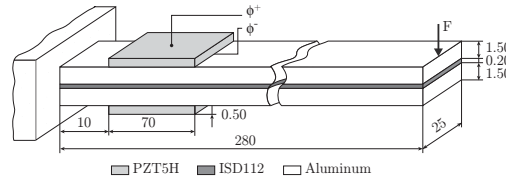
Caractéristiques de la poutre sandwich (en mm)
